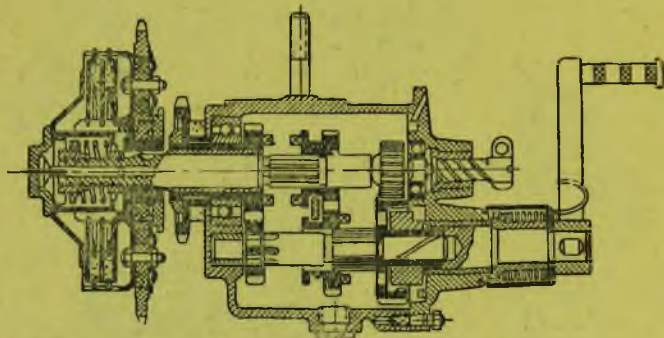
Положения в коробке передач Л-300, ИЖ-7, ИЖ-8, Л-8
